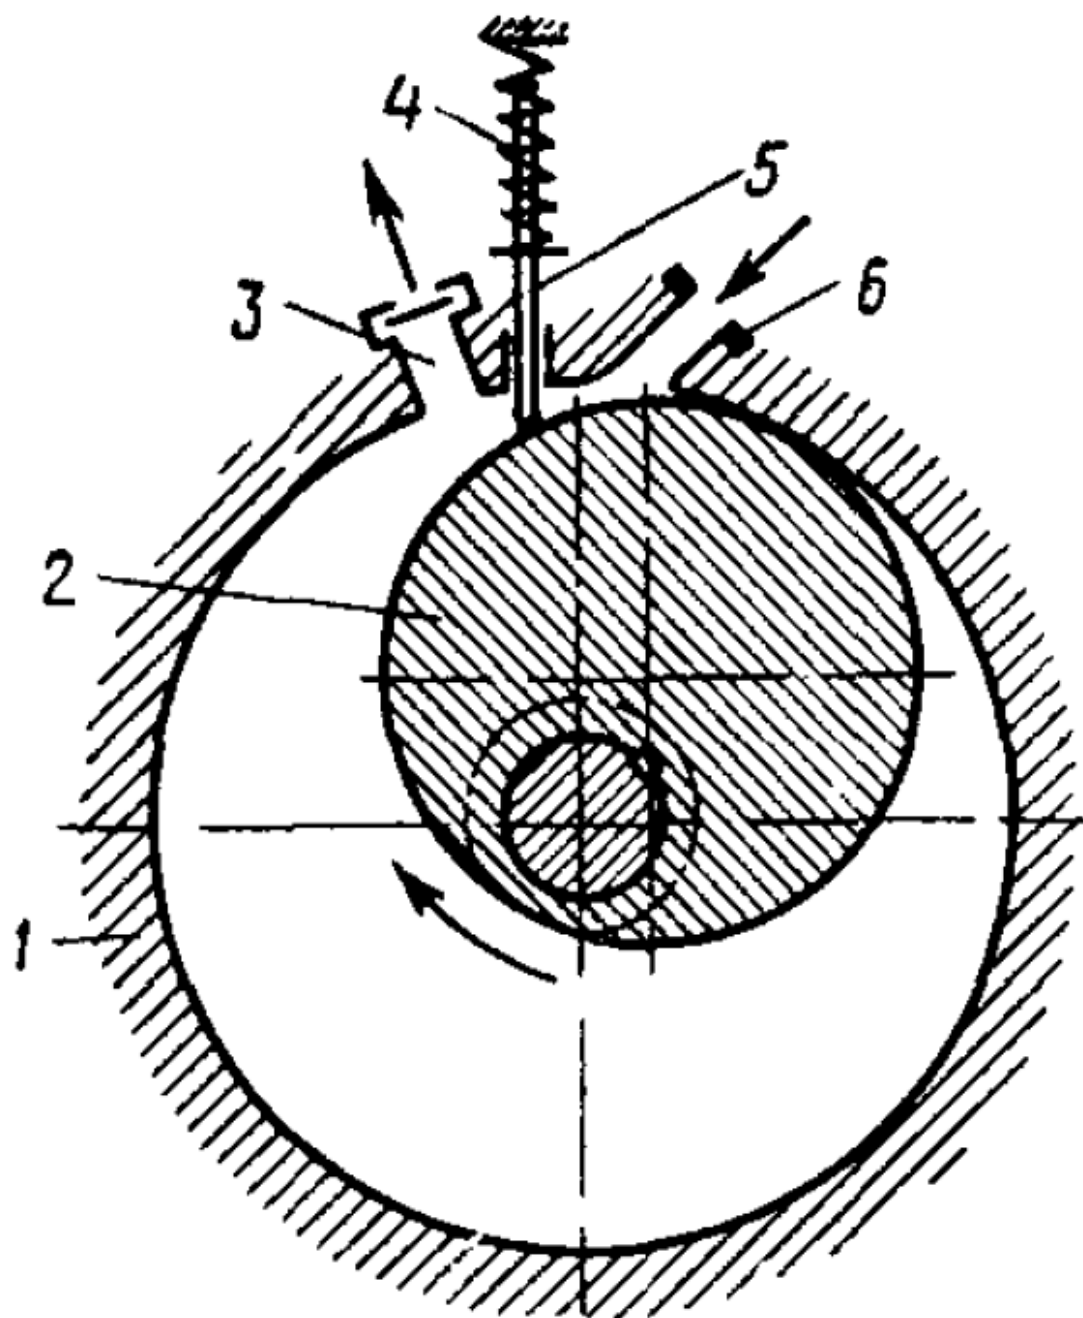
Устройство пластинчато-статорного насоса. 1 – цилиндрический корпус; 2 – эксцентрический ротор; 3 – выпускной патрубок с клапаном; 4 – пружина; 5 – пластина; 6 – входной патрубок [7, с. 166]
